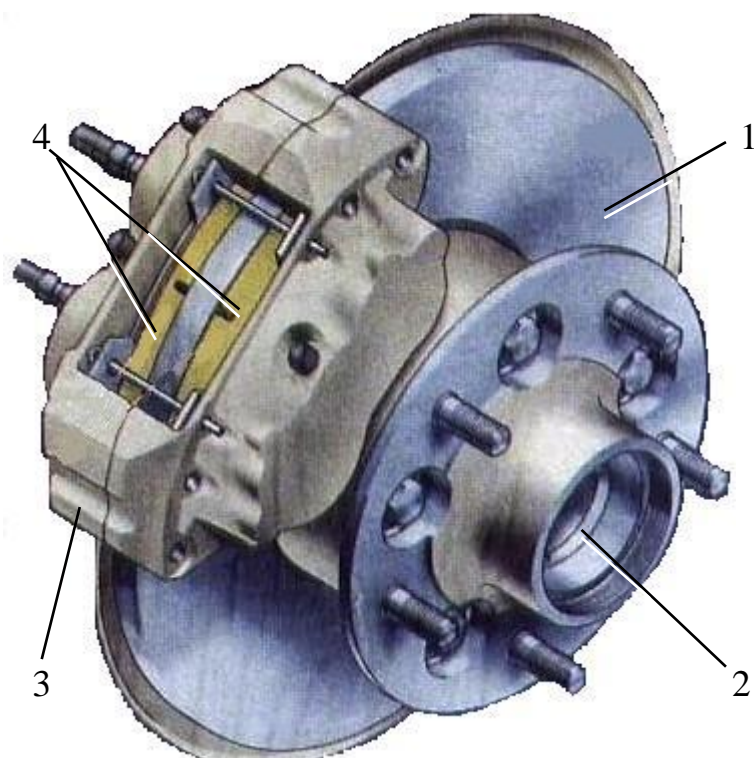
Дисковый тормозной: 1 – тормозной диск; 2 – ступица колеса; 3 – суппорт; 4 – тормозные колодки
